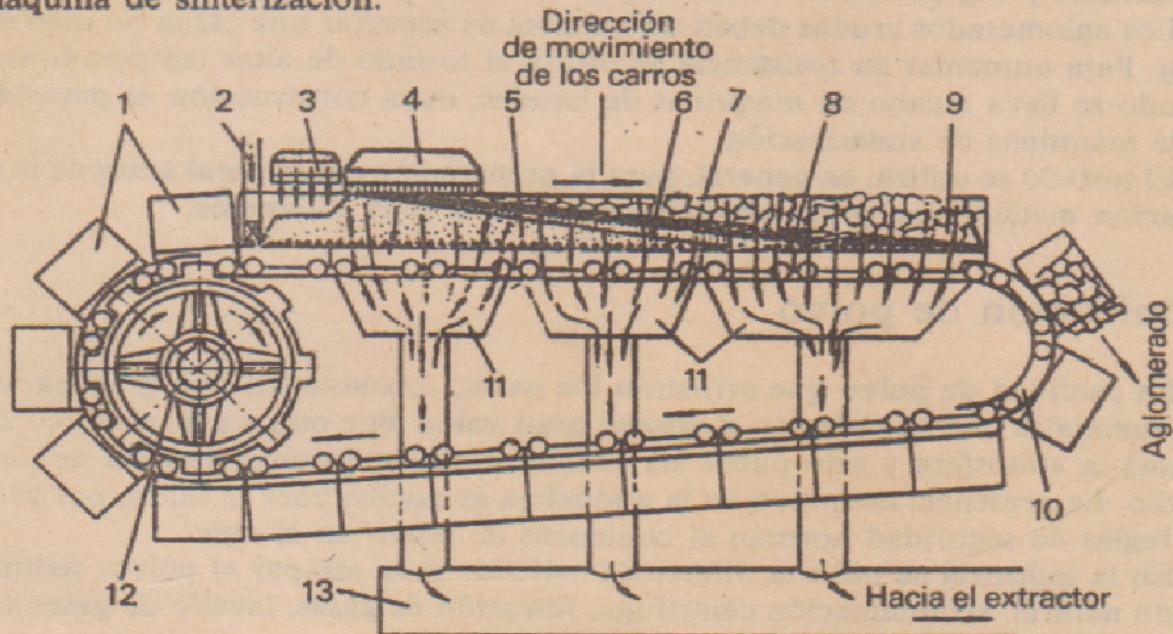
Máquina de aglomeración: 1) carretillas; 2) colador de capa; 3) colador de carga; 4) horno de encendido; 5) capa de la cama; 6) carga seca; 7) zona de calentamiento; 8) zona de combustión del combustible sólido; 9) zonas del aglomerado preparado; 10) rieles guías; 11) cámara de vacío; 12) engrane motor; 13) colector de gas
